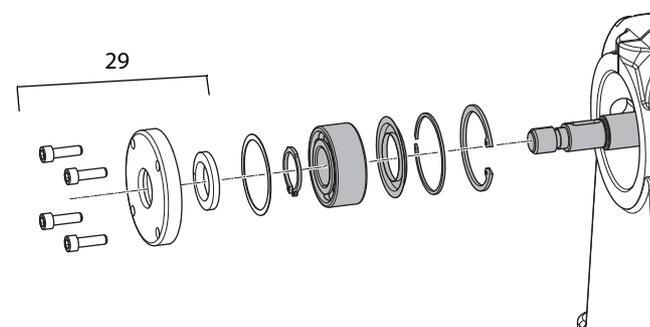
Bauform L1, Pumpenwelle, pumpenseitig
